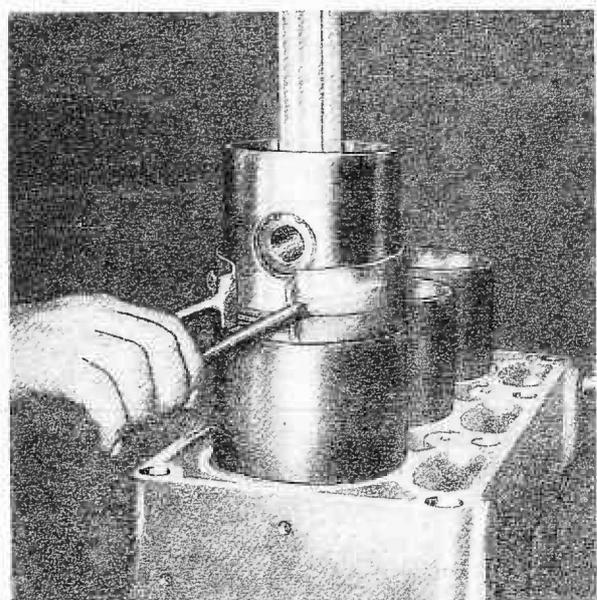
Einbau des Kolbens mit Kolbenringschelle
